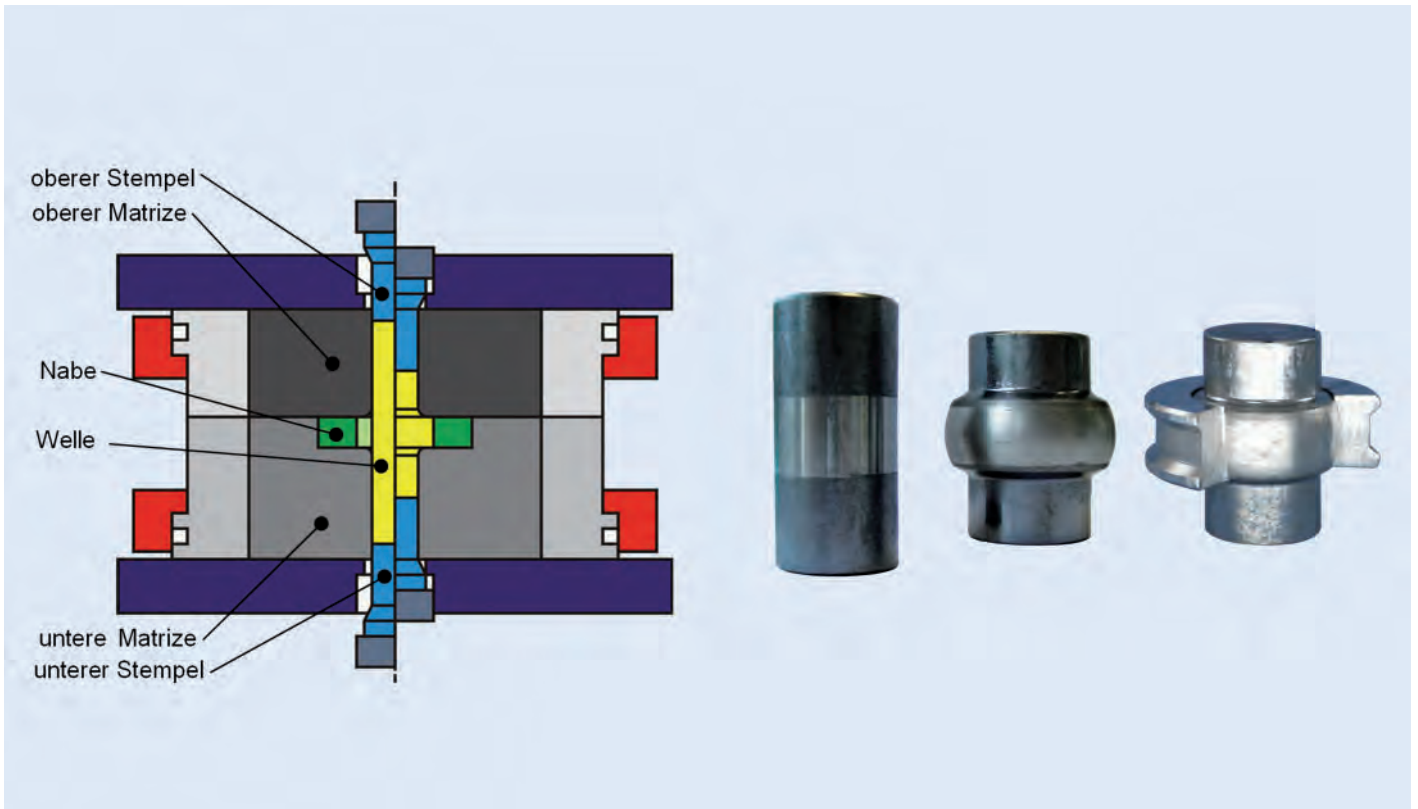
Links: Aufbau des Werkzeugs im Querschnitt. Rechts: Schmierstoffverteilung auf dem Wellenkörper (Zustellmuster ohne Nabenrohteil) und umformtechnisch gefügte Welle-Nabe-Verbindung.
